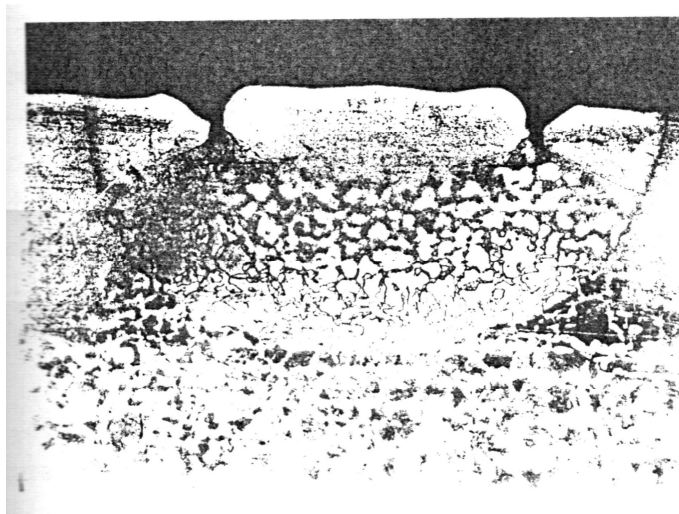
Основа – сталь 45, добавочный металл – проволока марки 45.
